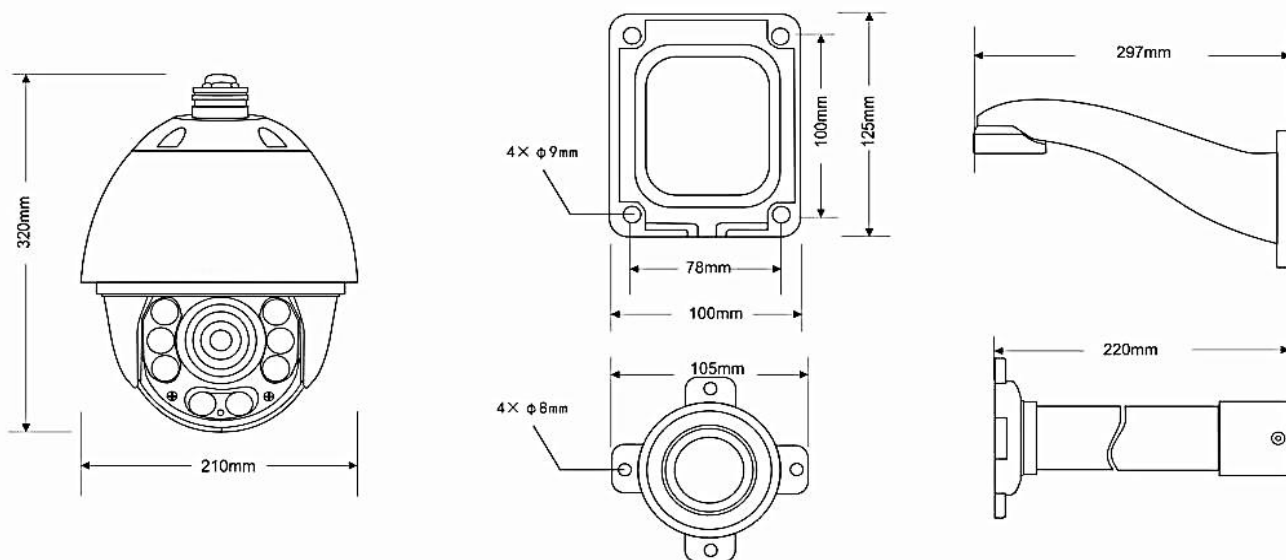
Габаритный чертеж видеокамеры ИВМ-711.
